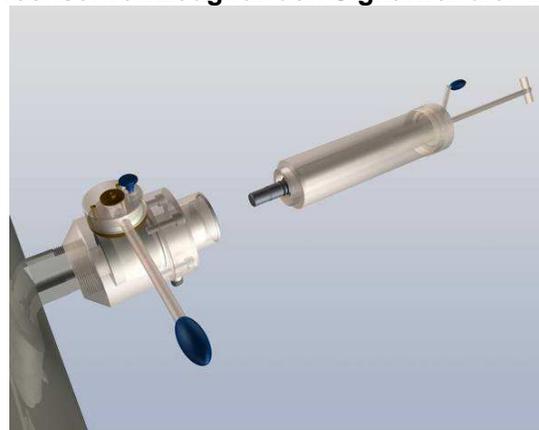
Wandlerwechselwerkzeug für den Signalwandler in Ausbau-Position
